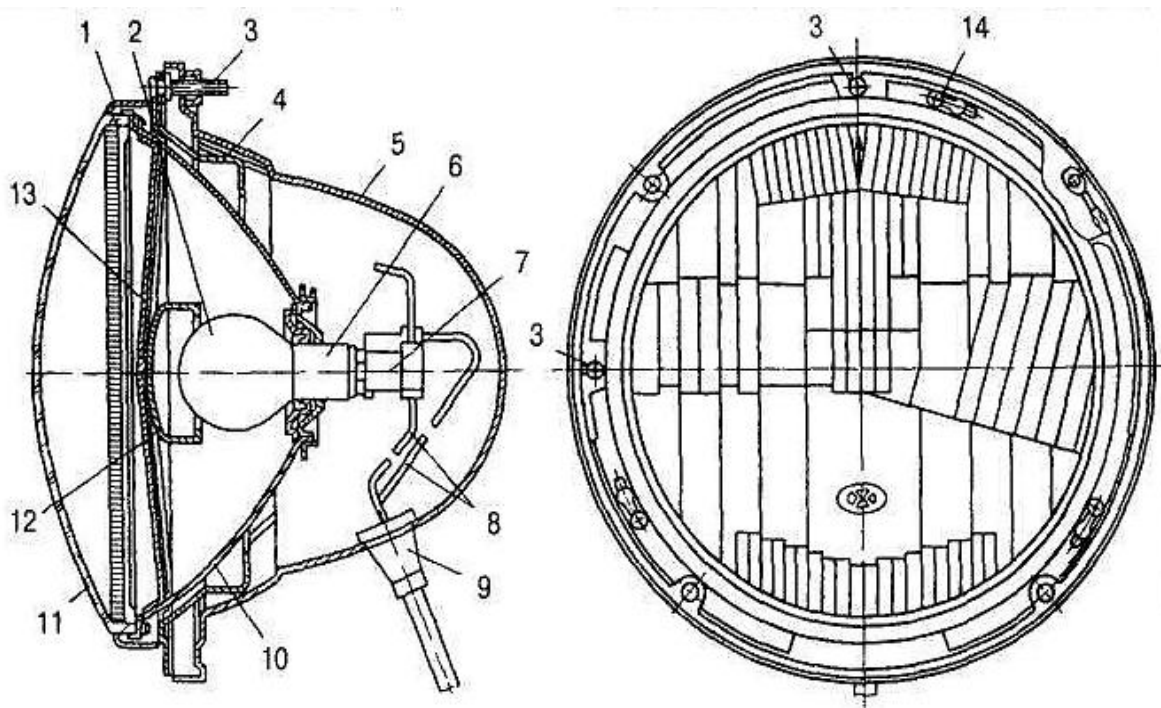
Принципова схема конструкції фари ФГ140:
